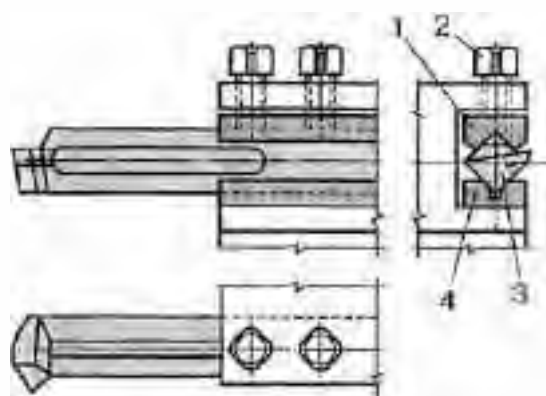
ЖОРСТКИЙ РОЗТОЧУВАЛЬНИЙ РІЗЕЦЬ В. К. СЕМІНСЬКОГО
